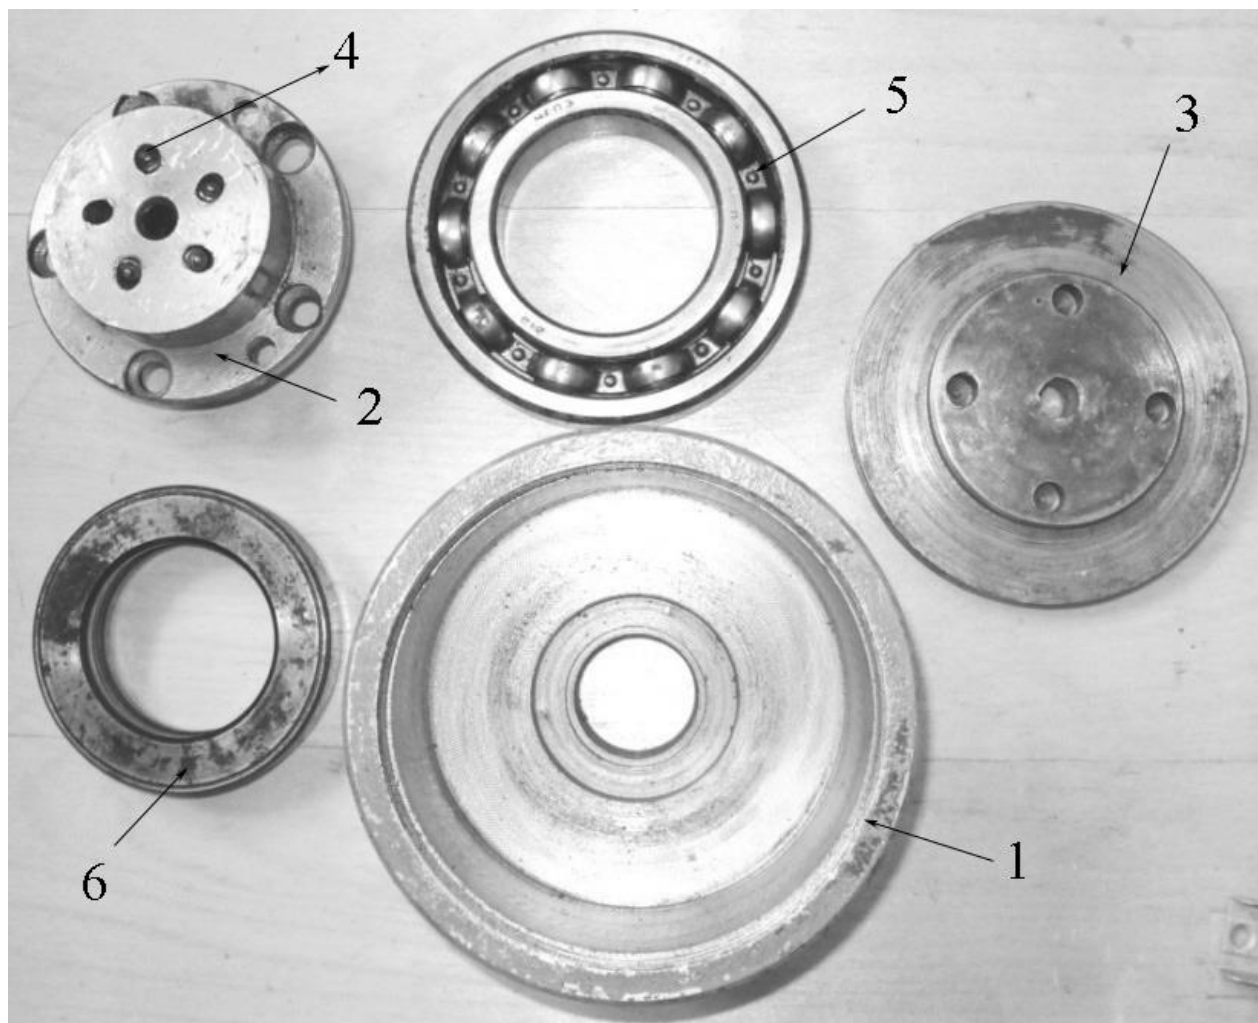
Чертеж разработанной конструкции волоки для получения винтовых профилей
